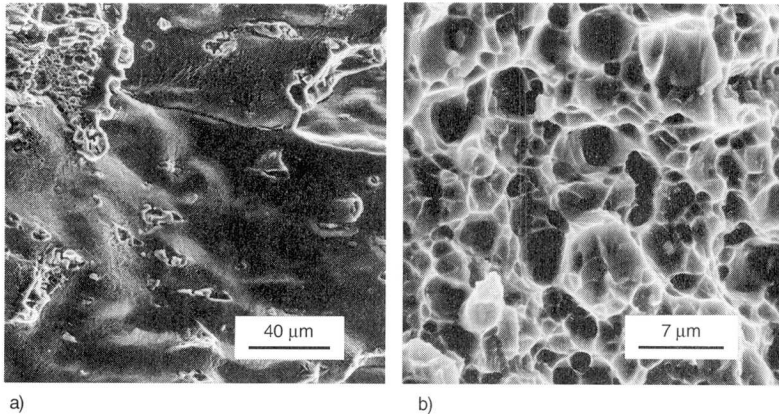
Fraktographie (REM); a) P240-T6X; b) P213-T6X
